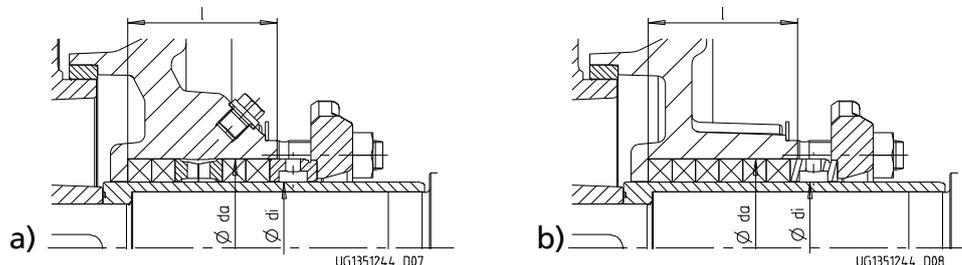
Набивочная камера сальника а) с блокировочным кольцом и б) без блокировочного кольца
